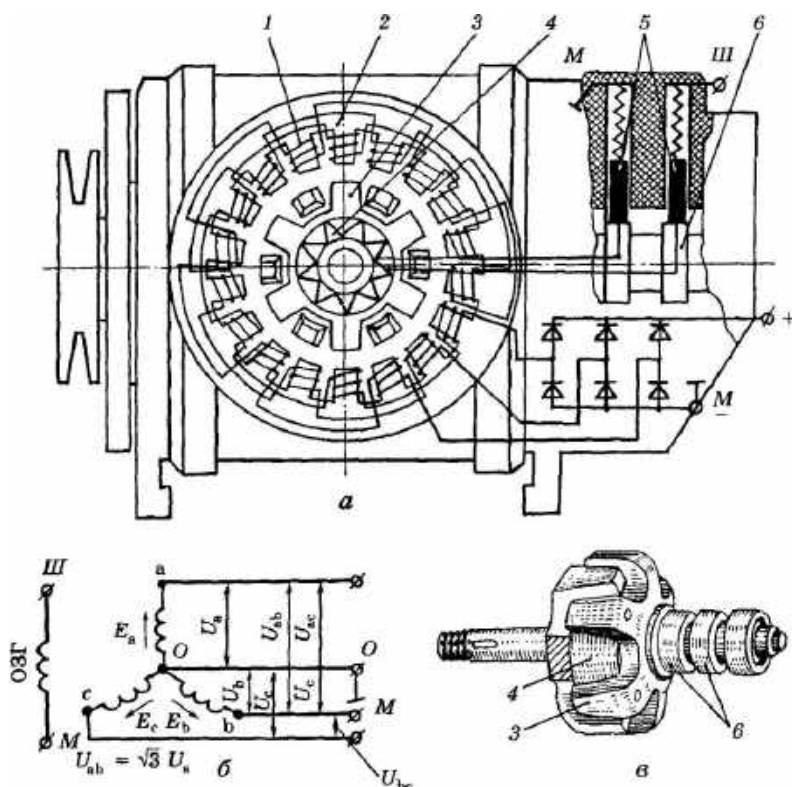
Схема генератора з рухомою обмоткою збудження: а — принципова схема; б — електрична схема; в — ротор; 1 — обмотка котушок статора; 2 — статор; 3 — полюси ротора; 4 — обмотка збудження; 5 — щітки; 6 — , контактні кільця
